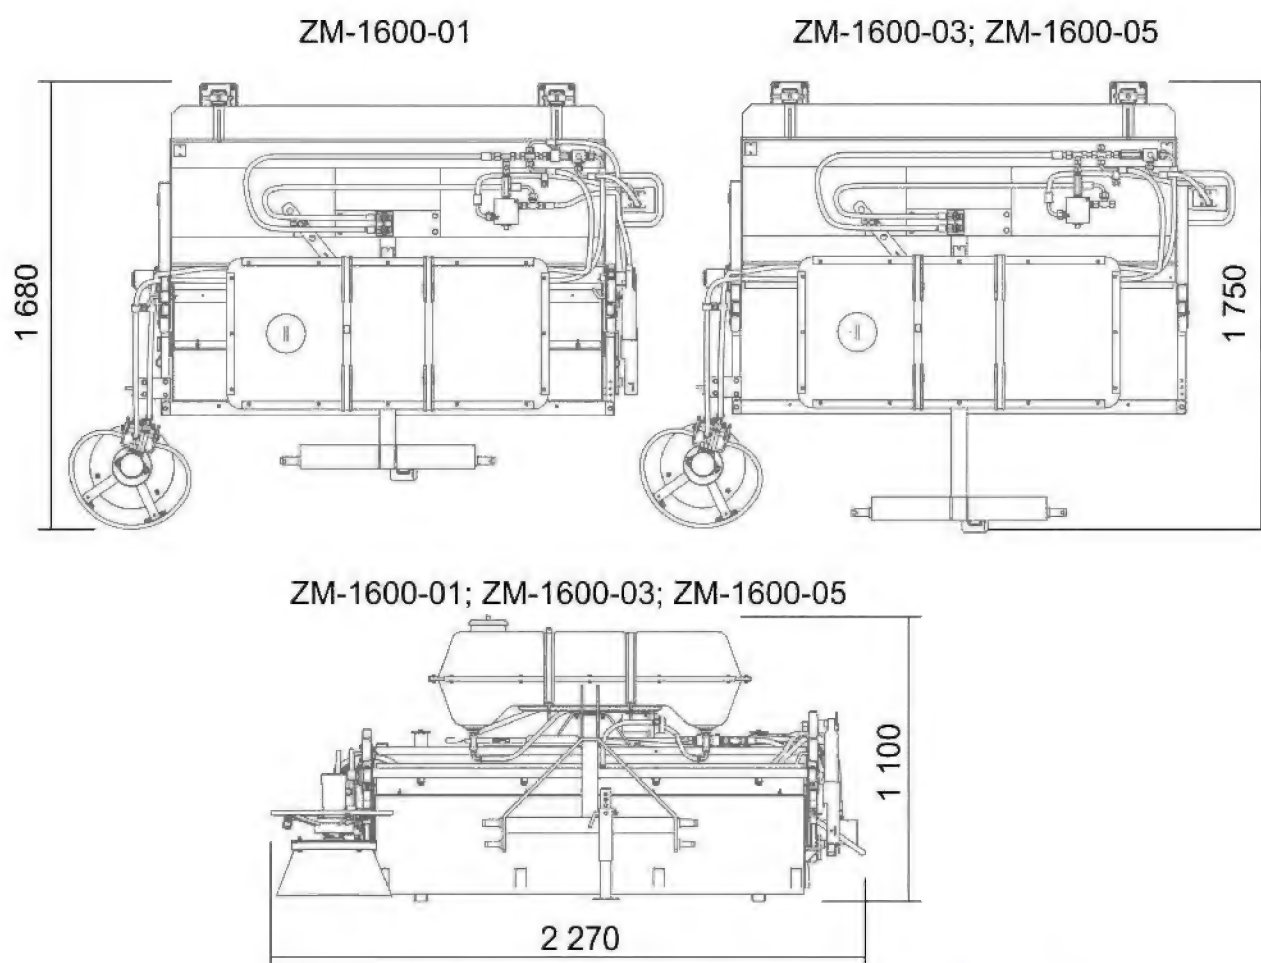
A Dimensions externes ZM-1600-01; ZM-1600-03; ZM-1600-05
